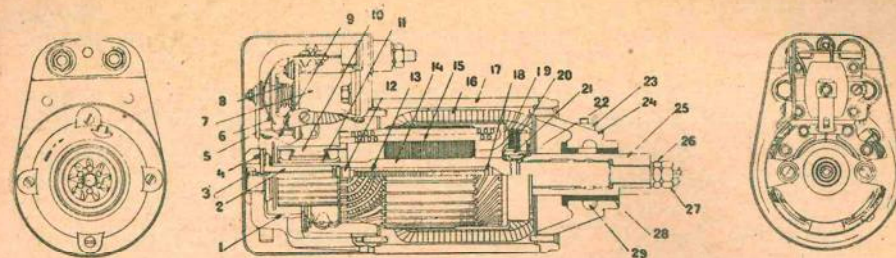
Общий вид стартера СМА 2,5 л/с.
